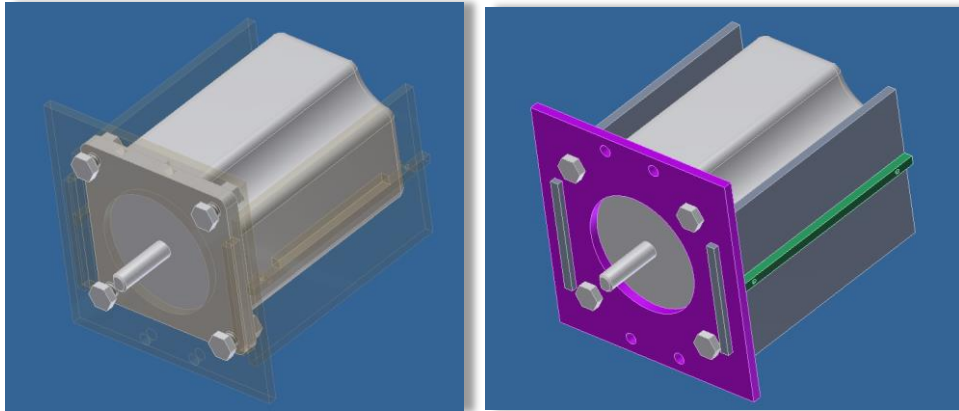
Porta motor (izquierda) y piezas que lo componen (derecha).
